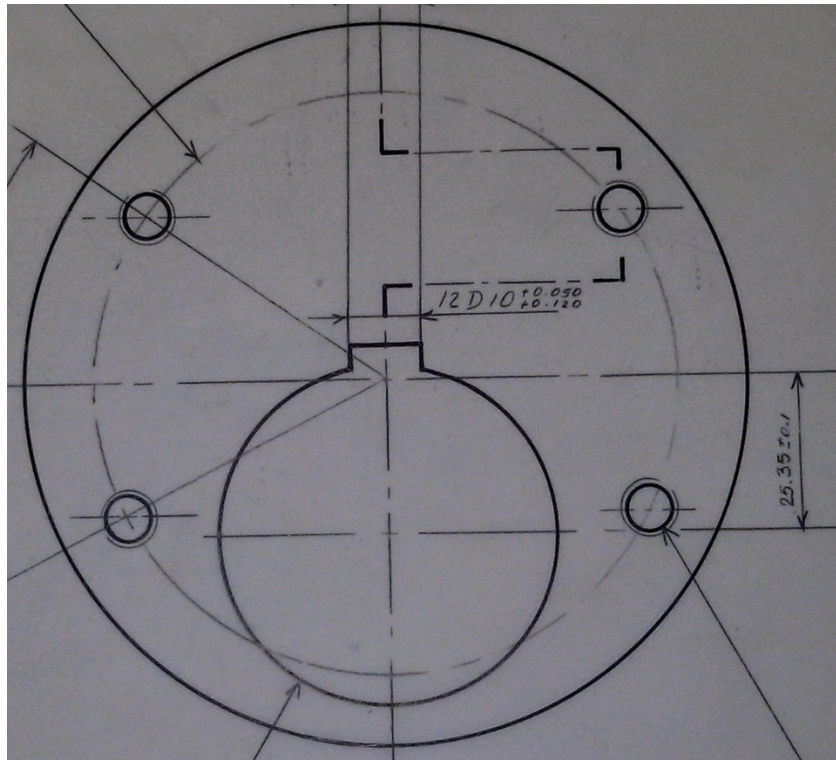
Altura de la pieza A3-004 Excéntrica.
